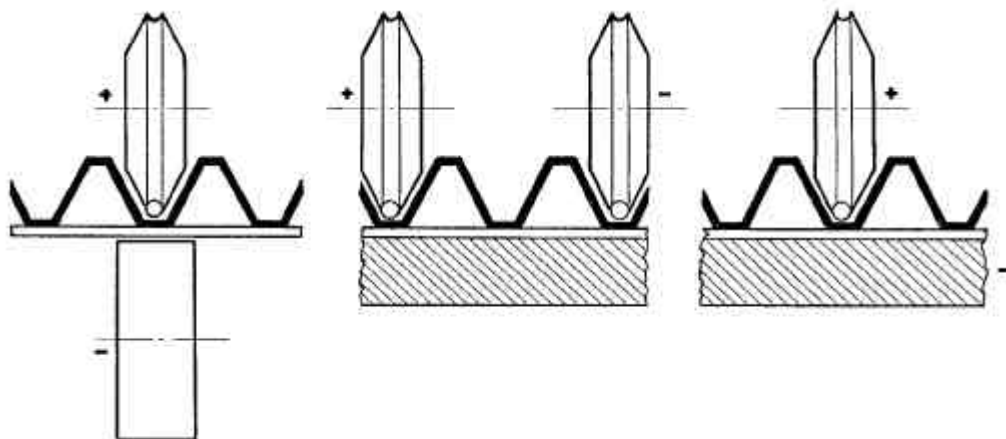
Possibili configurazioni nella saldatura con rulli.
